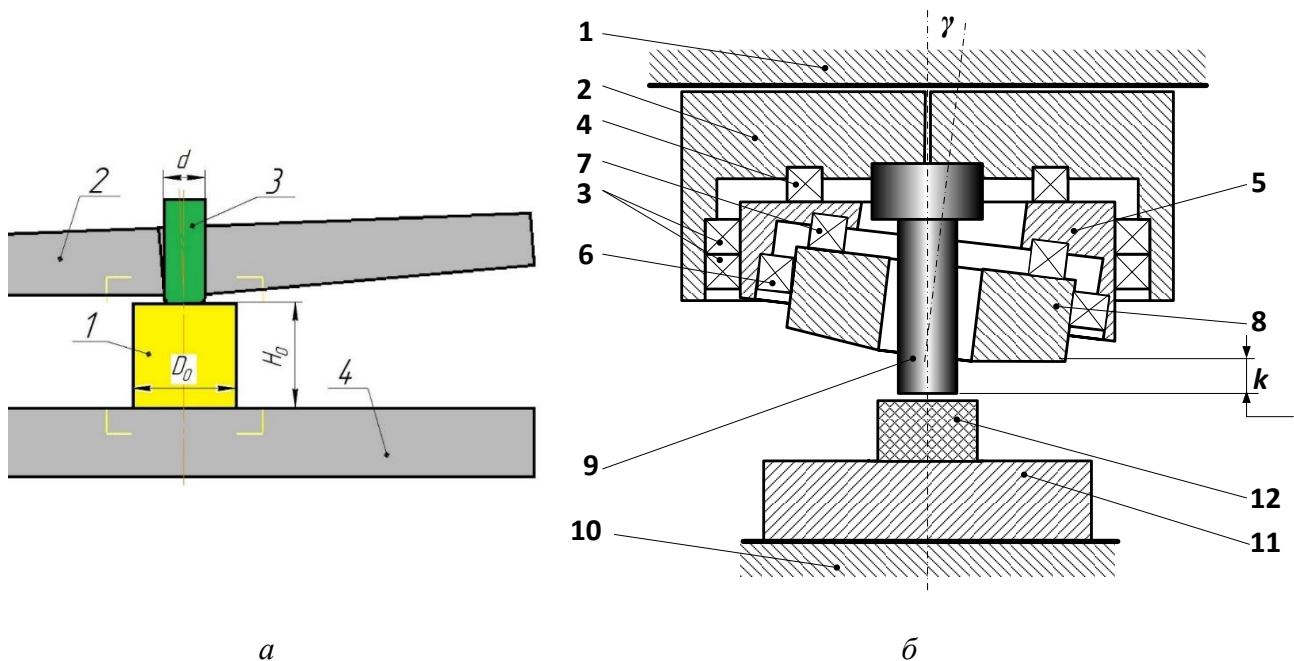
Схема процесу та пристрою для суміщеного штампування обкочуванням та прошивання процесу (1 – заготовка; 2 – обкочувальна головка; 3 – центральний прошивний пуансон, що виступає на задану глибину порожнини $k=2\text{мм}$; 4 – нижня плита; H_0 та D_0 – висота та діаметр циліндричної заготовки; d – діаметр прошивного пуансону: 1 - повзун пресу; 2 – корпус; 3,6 – радіальні підшипники; 4,7 – упорні підшипники; 5 - ротор; 8 - обкочувальна головка; 9 - прошивний пуансон; 10 - стіл пресу; 11 - опорний інструмент; 12 - циліндрична заготовка; k – величина виступу прошивного пуансону; γ – кут нахилу осі обкочувальної головки): а – розрахункова схема суміщеного процесу; б – конструктивна схема пристрою
